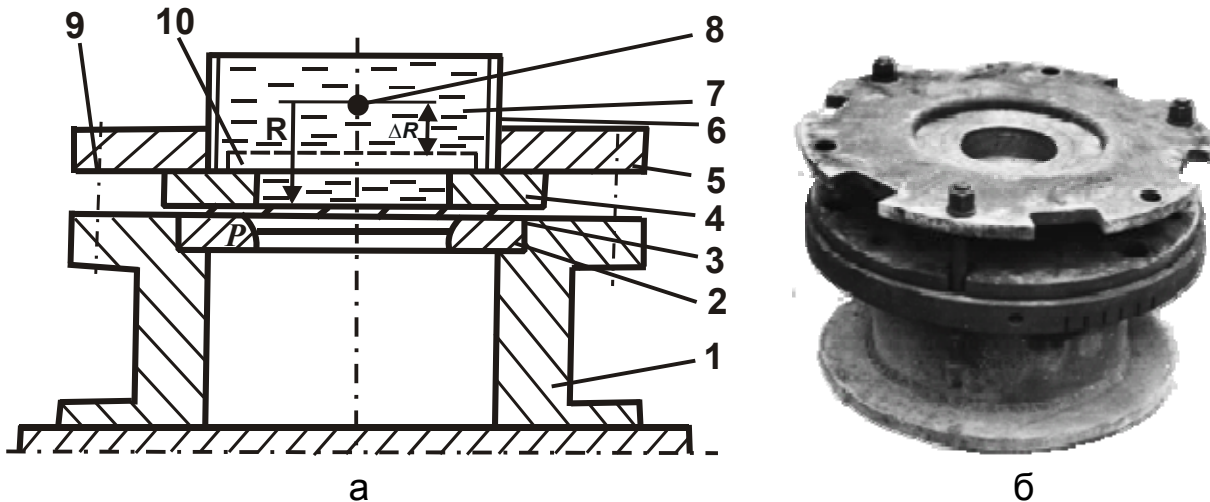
Схема (а) і загальний вигляд (б) установки для штампування тонкостінних деталей
